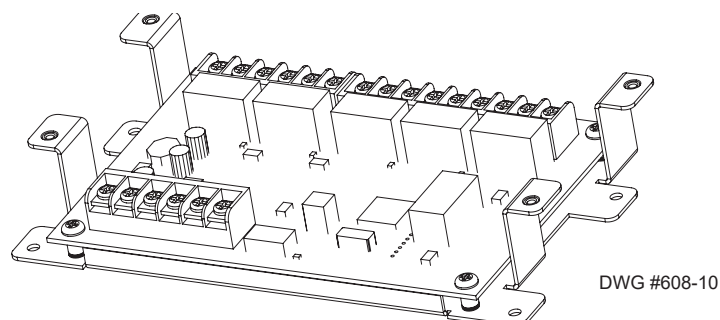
Placa RLY-5 que muestra el soporte de montaje
